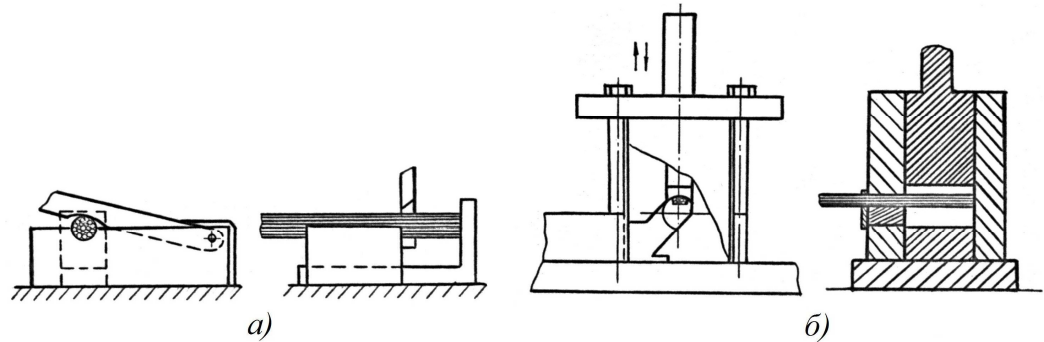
Способы резки проволоки в пучках: а) резка ножницами; в) рубка в штампе
